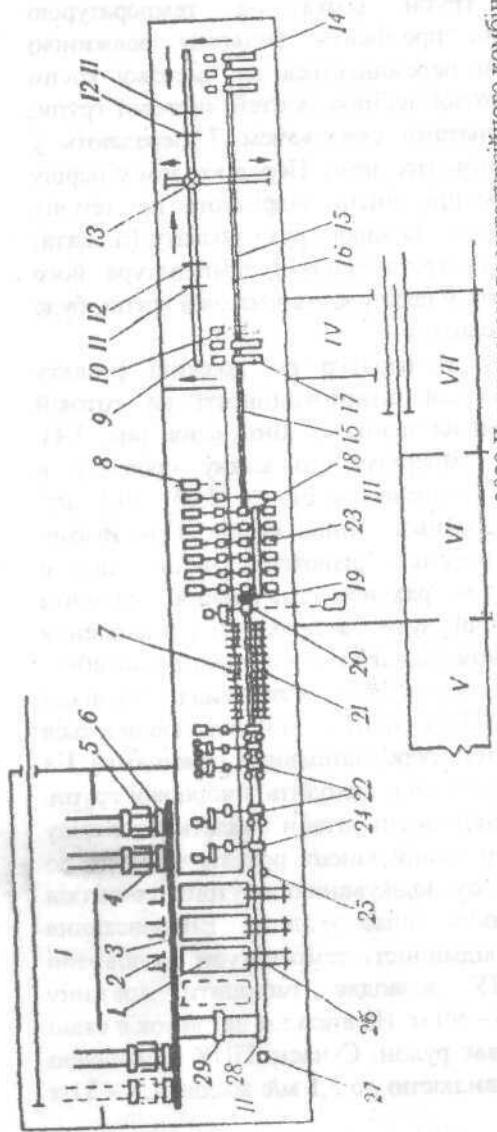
Схема розташування обладнання стани 2030 Череповецького металургійного комбінату: I- склад слябів; II-проїзд стана; III-ділянка підтримання валків; IV-насосна станція; V-мастерня ревізій підшипників кочення; VI-вальцепрессувальна мастерня; VII-склад валків; 1-нагрівальна піч; 2- штовхач слябів у пічі; 3-завантажувальний рольганг; 4-візок для слябів; 5-штовхач слябів у столі; 6- підйомний стіл; 7-зкидувач недокатів; 8-чистова кітль №8 (штриховими лініями показана нагрівальна піч і чистова робоча кітль №8, намічені до установки); 9-конвеєр рулопів; 10-кантувальний ролон; 11-марсривальник рулонів; 12-рулоно-в'язальна машина; 13-підйомно-поворотний стіл; 14-рулонів; 15-системи охолодження штаб на відділних рольгангах; 16-відвідні рольганги; друга група моталок; 18-чистова група кітей; 19-чистовий роликовий окалиноломач; 20-легучі 17-перша група моталок; 22-горничи чистовий роликовий универсальний кіті; 23- полож; 21-карман для недокатів і товстих штаб; 25-чорнова кітль; 26-приймач слябів; 27- механізми для зміни валків; 24-чорнова кітль; 25-вертикальна кітль; 26-приймач слябів; 27-стационарний упор; 28-приймальний рольганг для слябів; 29-передраточний візок для слябів.
